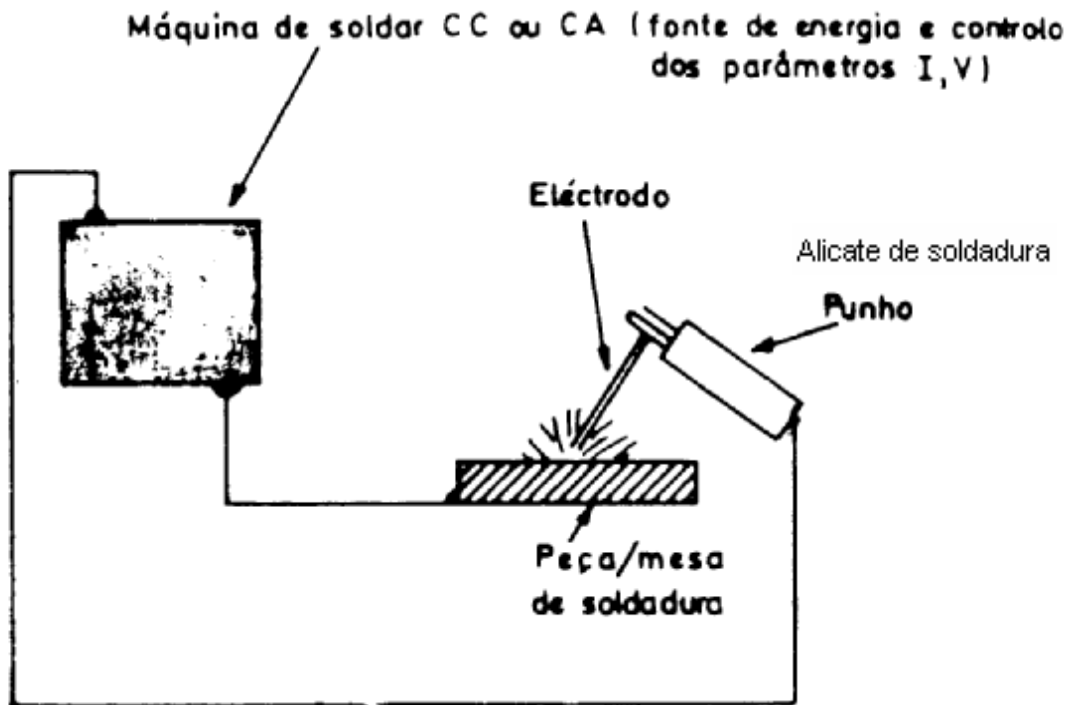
Circuito básico de soldadura por arco eléctrico
